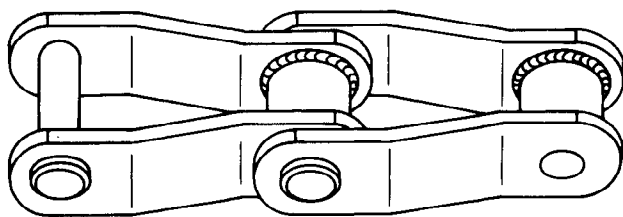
Chaîne à maillons soudés assemblée
